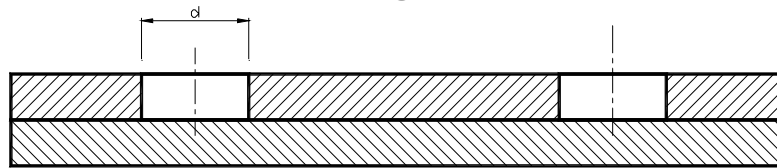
Desenho esquemático de corpos de prova a serem soldados em laboratório.
